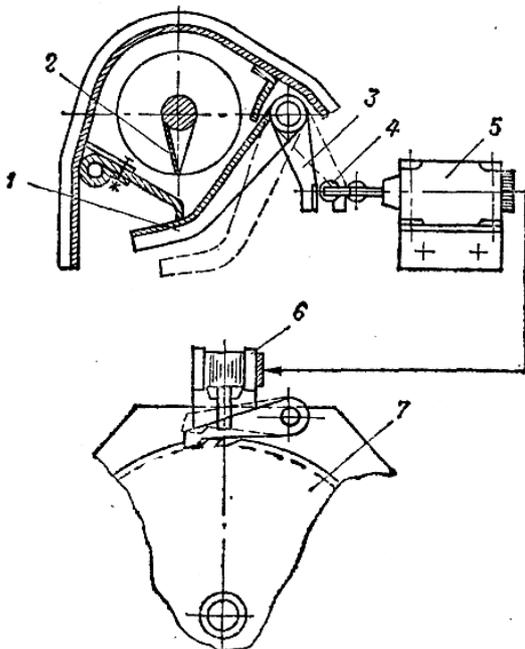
Автоматический регулятор подачи материала (загрузки): 1- клапан – питатель; 2 – распределительный шнек; 3 - отключающий упор; 4 – ролик; 5 – конечный выключатель; 6 – электромагнитное устройство; 7 – механизм самопередвижения
